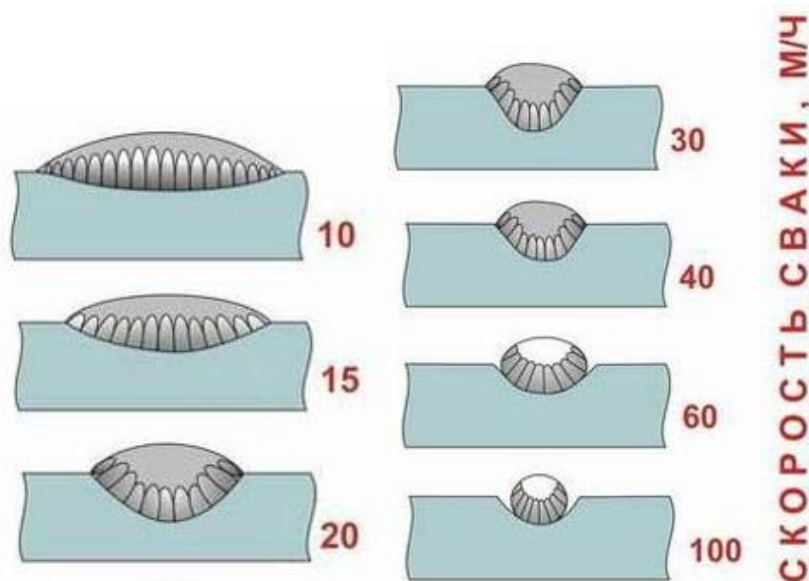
Влияние скорости сварки на форму сварного шва
